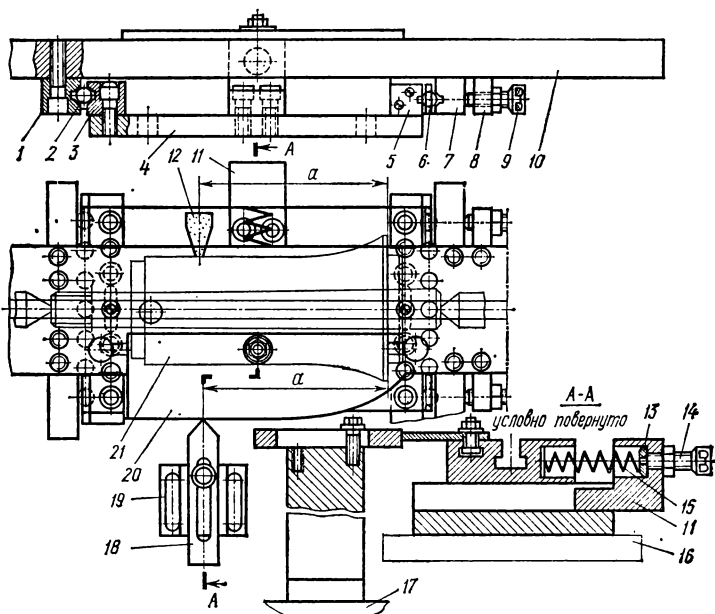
Приспособление для заточки фрез с острозаточенными зубьями
